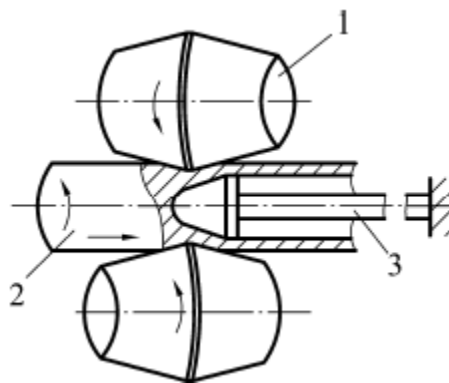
Схема прошивки заготовки при поперечно-винтовой прокатке
